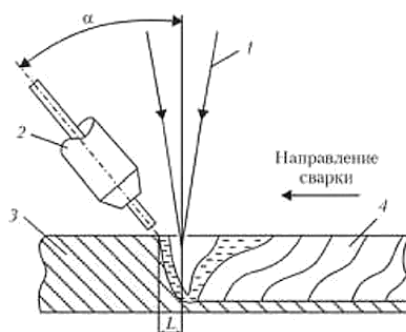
Схема гибридной лазерно-дуговой сварки: 1-фокусирующее лазерное излучение, 2-плавящийся электрод, 3-свариваемый образец, 4-шов.
